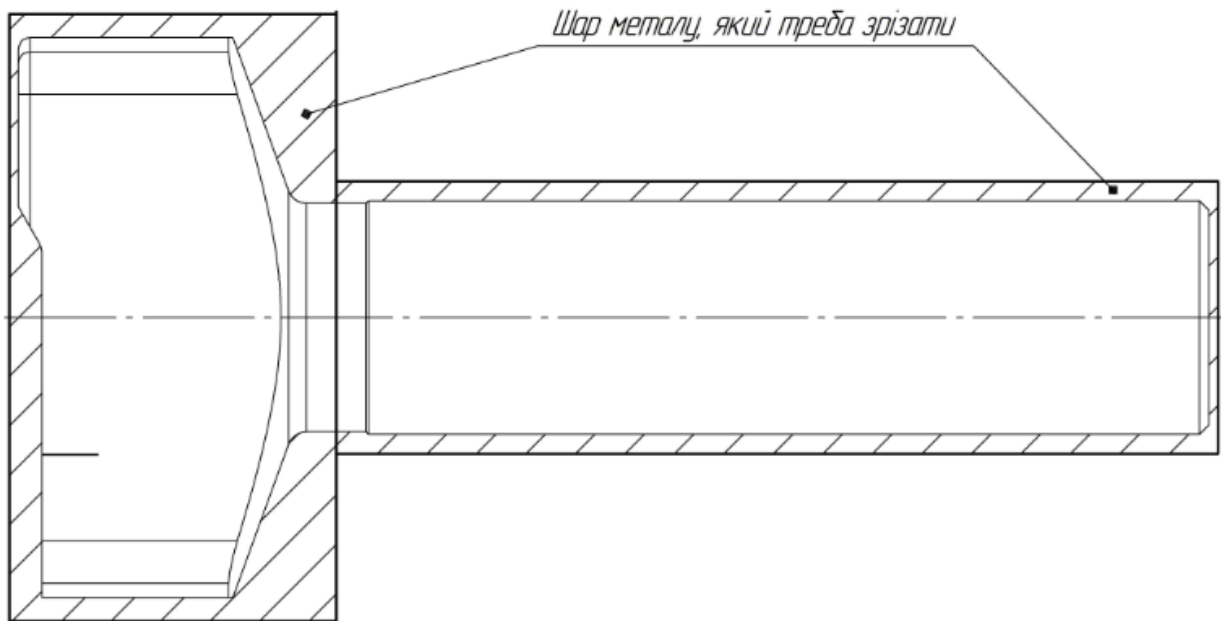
Заготовка зі зварених двох частин прокату
